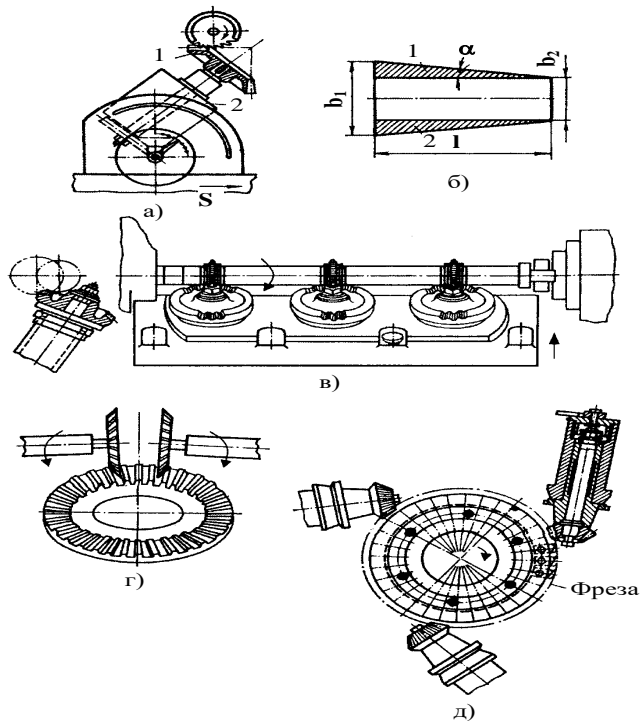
Зубофрезерування конічних зубчастих коліс:
